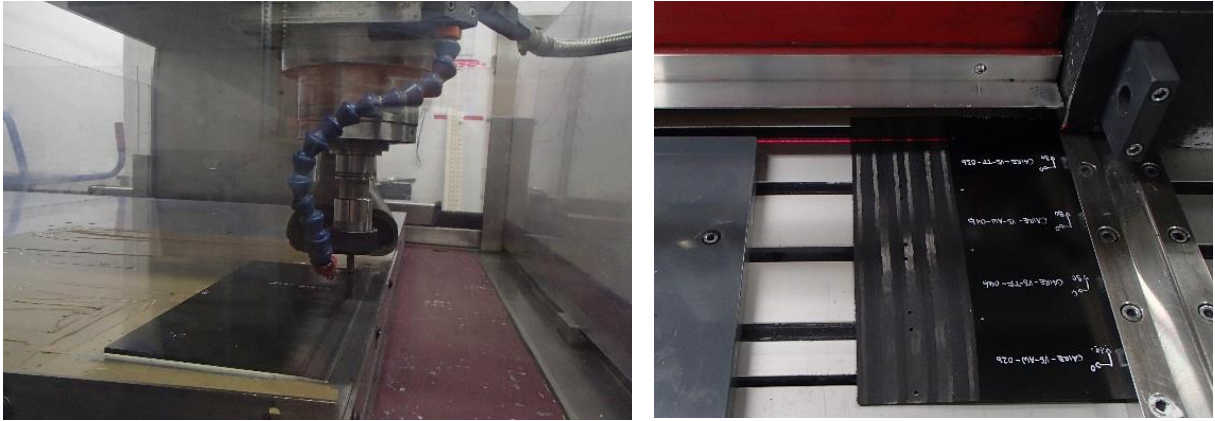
Fräsen der Schäftungen (links) und Zuschnitt der Proben mit einer Diamantsäge (rechts)
